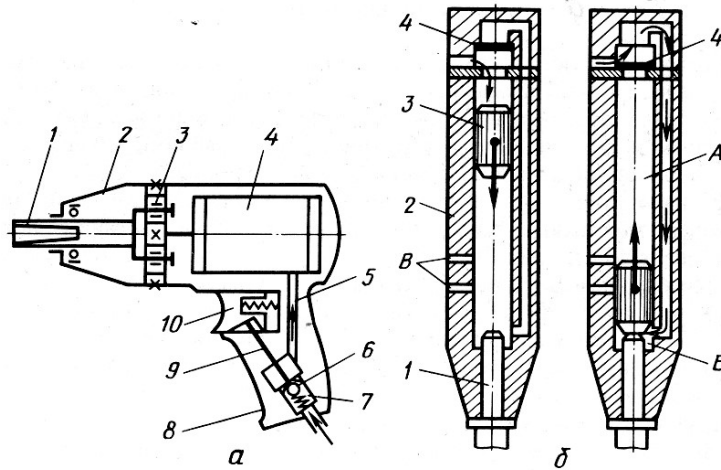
Схеми пневматичних ручних машин: а – свердлильної: 1 – шпindelь, 2 – корпус, 3 – редуктор, 4 – пневмодвигун, 5 – канал підведення стиснутого повітря, 6 – клапан, 7 – пружина, 8 – рукоятка, 9 – штовхач, 10 – курок, б – відбійного молотка: 1 – інструмент, 2 – ствол, 3 – поршень-бойок, 4 – повітророзподільний пристрій, А, Б – камери робочого і холостого ходу поршня: В – канал для випуску відпрацьованого повітря в атмосферу
